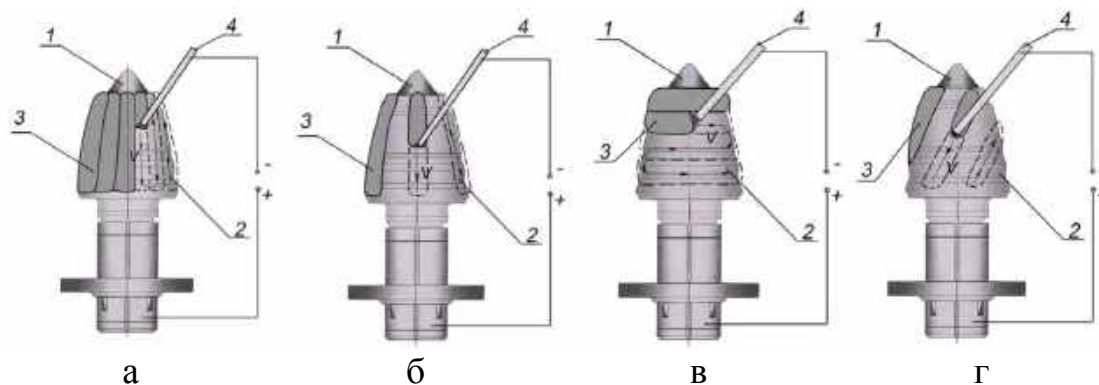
Технологічні схеми наплавлення різців дорожніх фрез [2]: а – паралельно осі різця; б – паралельно осі з зазорами; в – під кутом до осі; г – спіралеподібне наплавлення: 1 – наконечник різця; 2 – корпус різця; 3 – наплавлений метал; 4 – контури накладання валиків; V – напрямок наплавлення
